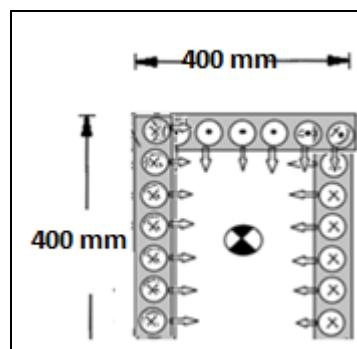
DIMENSIONAMIENTO DEL CORDÓN DE SOLDADURA EN LOS TUBOS.
